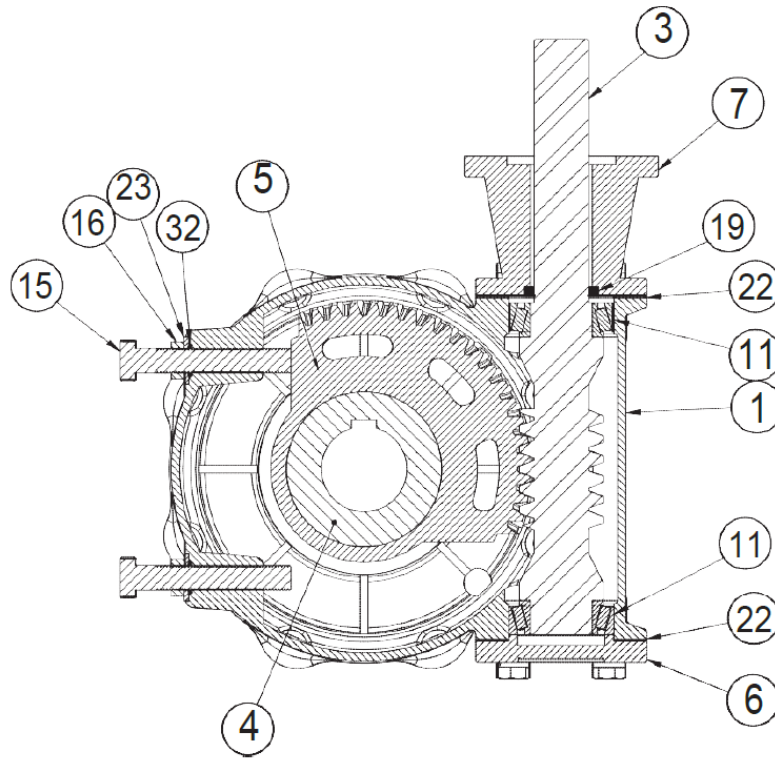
SBWG-00 bis SBWG-35 Baugruppenansicht
